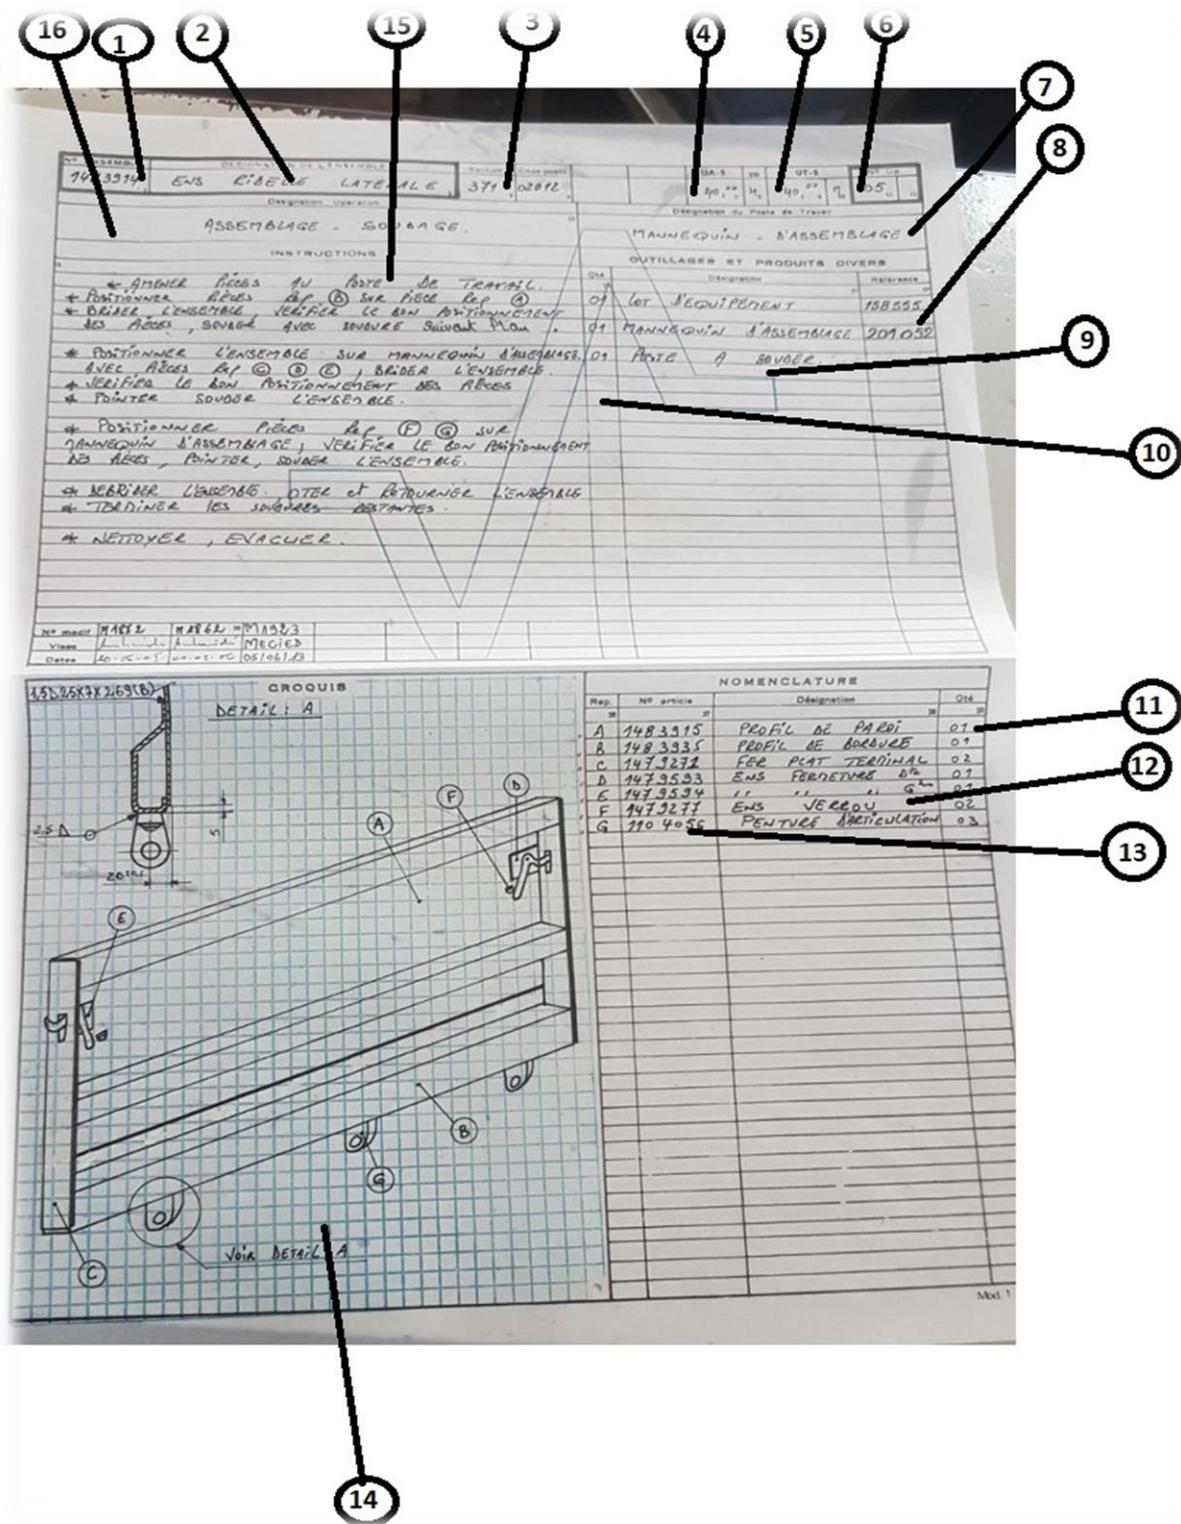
photo de FOLIO de ridelle latérale de camion k120 C088
